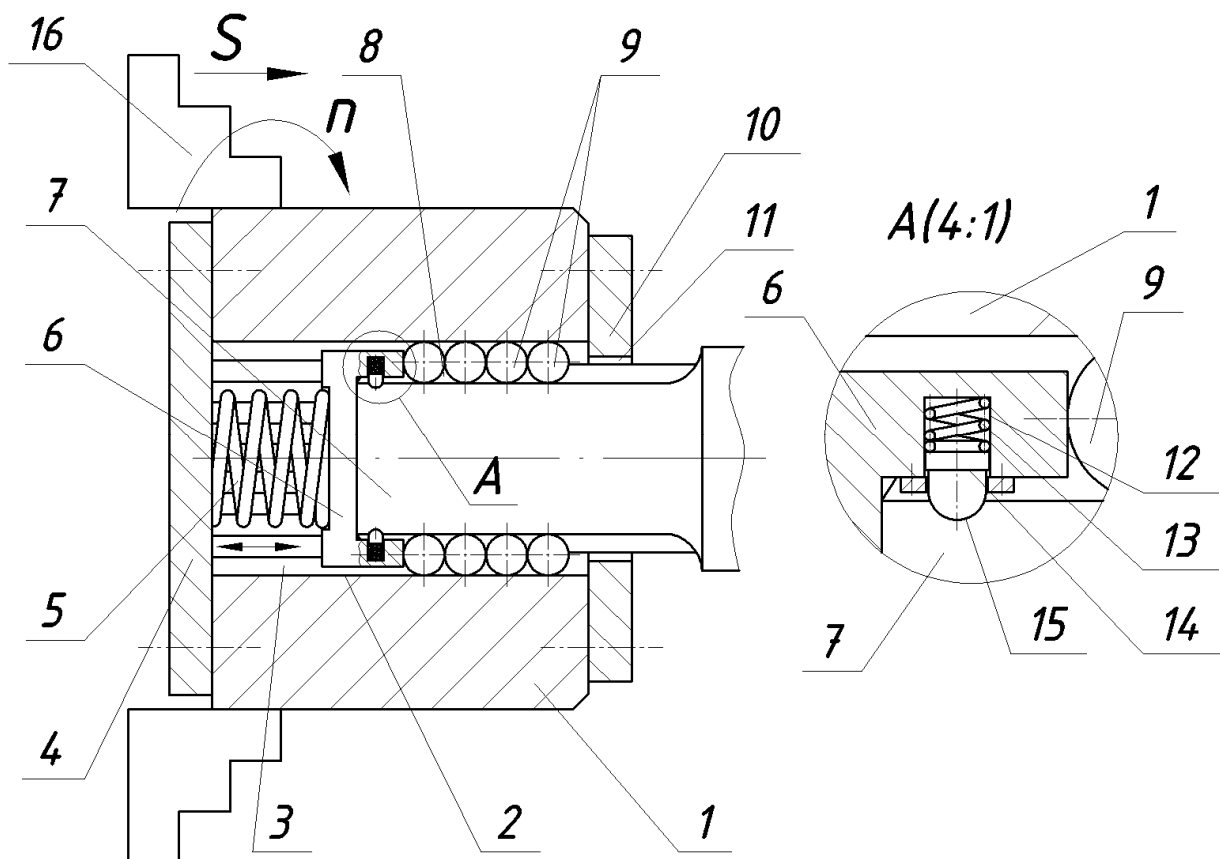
Самовстановлювальний пристрій для дорнування внутрішніх напівкруглих гвинтових канавок
